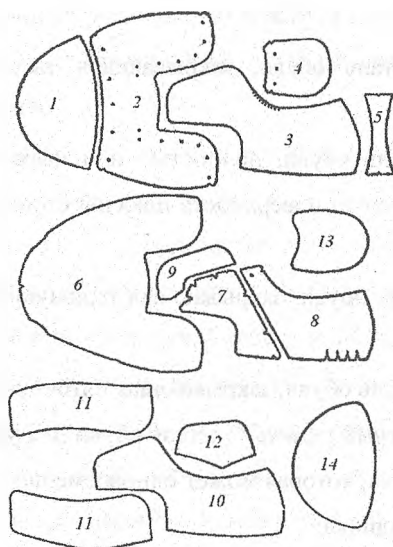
Детали заготовки полуботинка типа «конверт»:
